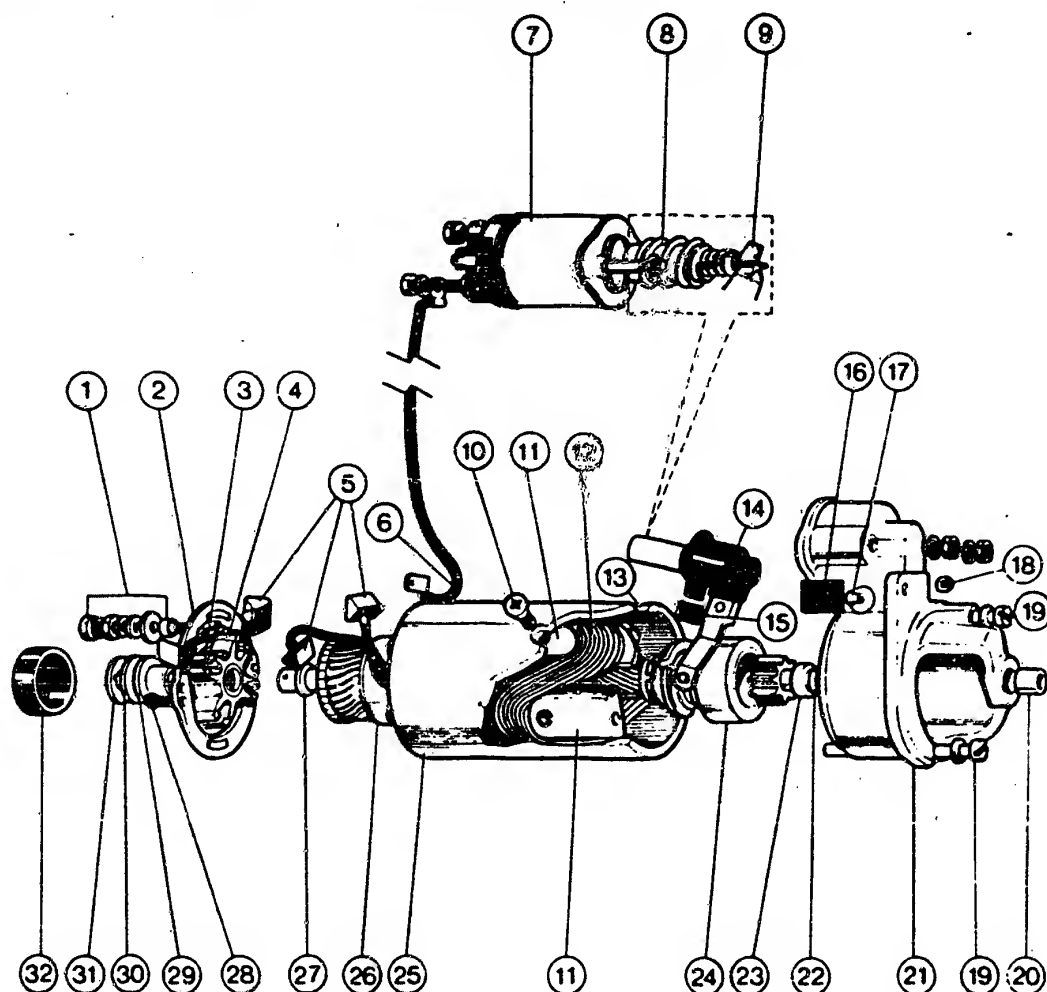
Lucas-Anlasser in seine Einzelteile zerlegt: 1 Anschluss-Befestigungsteile – 2 kollektorseitiges Lagerschild – 3 Bürstenhalter – 4 Bürstenfeder – 5 Kohlebürsten – 6 Verbindungskabel zum Magnetschalter – 7 Magnetschalter – 8 Rückholfeder – 9 Einrückgabel – 10 Polschuhschraube – 11 Polschuh – 12 Feldwicklung – 13 Anschluss der Feldwicklung an Masse – 14 Dichtung – 15 Gummieinlage – 16 Dichtung – 17 Drehbolzen – 18 Zahnsicherung – 19 Befestigungsschrauben – 20 Lagerbüchse – 21 antriebsseitiges Lagerschild – 22 Sicherungsring – 23 Anlaufring – 24 Ritzelantrieb – 25 Polgehäuse – 26 Anker – 27 Anlaufscheibe – 28 Befestigungsschraube – 29 Lagerbüchse – 30 Anlaufscheibe – 31 Zahnsicherung – 32 Staubkappe.
